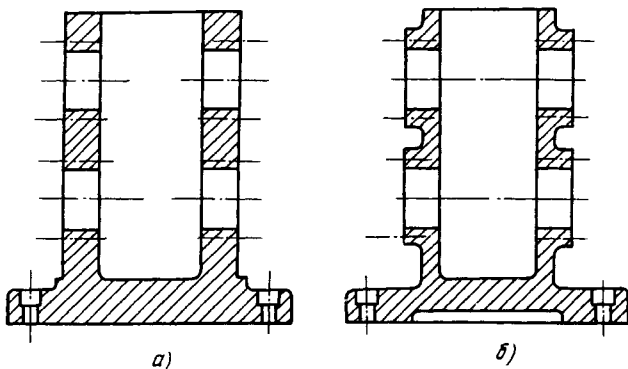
Два варианта конструкции корпусной детали с точки зрения металлоемкости
